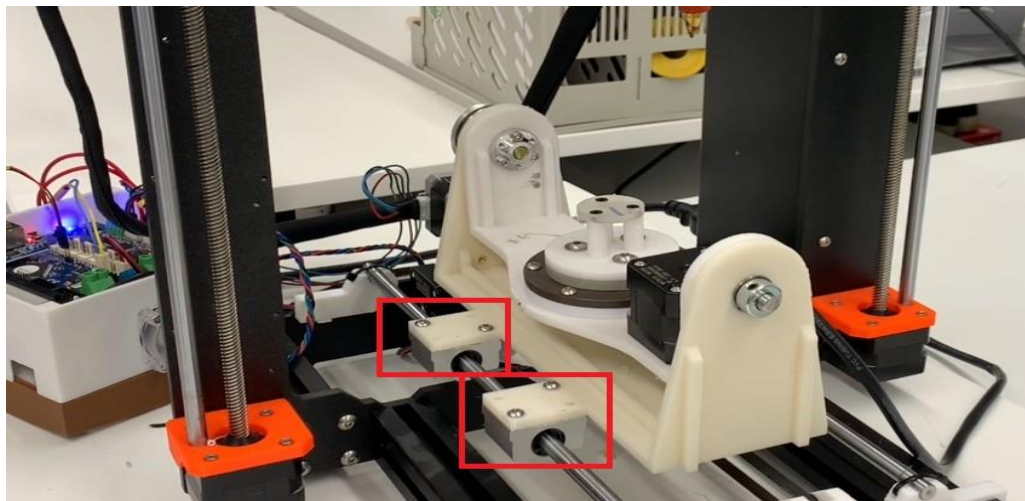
Ось Y та ковзаючі блоки лінійного підшипника в конструкції принтера
